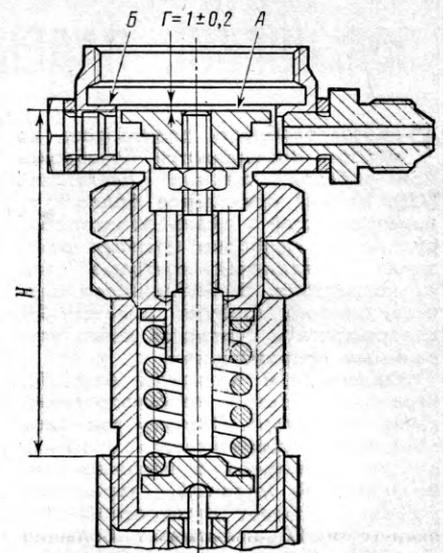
Регулировка размера Г при сборке форсунки с приставкой-догружателем
